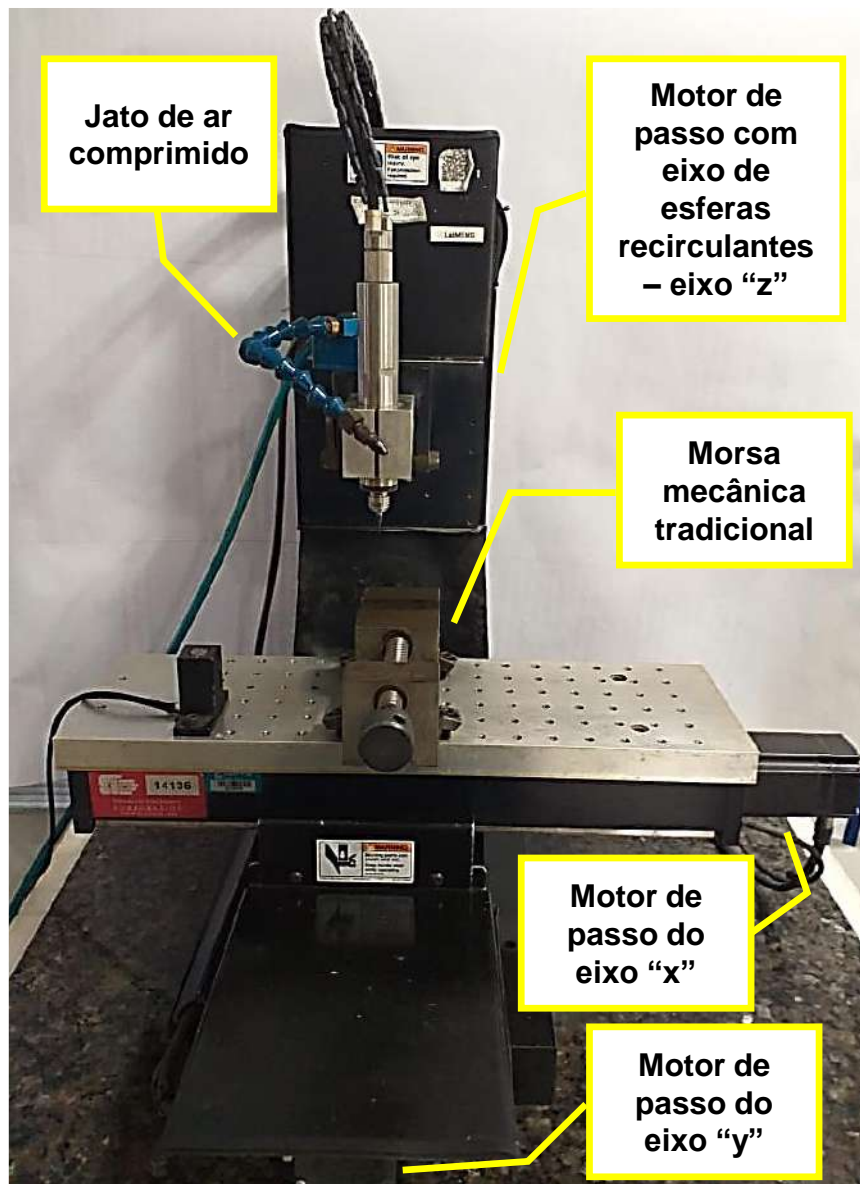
Microfresadora CNC Minitech Mini-Mill/OX
